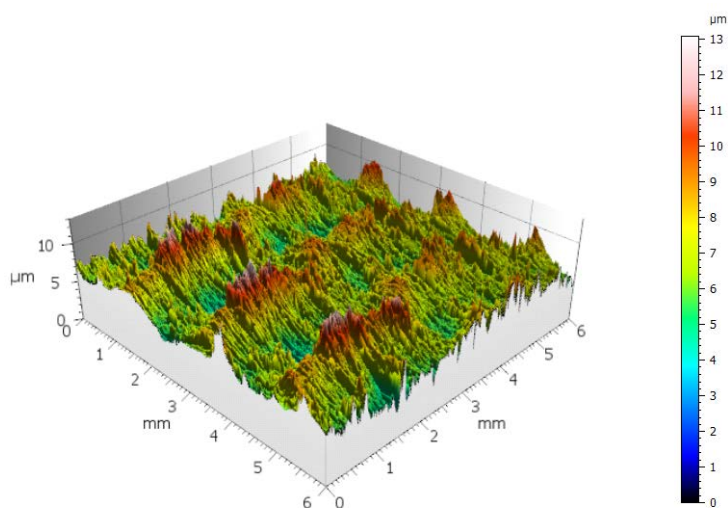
Топографія обробленої поверхні після фрикційної обробки інструментом з поперечними пазми на робочій поверхні
